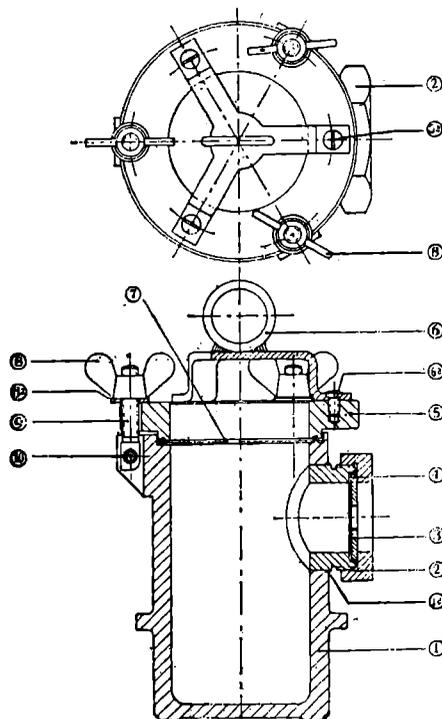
Recipiente a presión montado; vistas esquemáticas en sección vertical y en planta.
